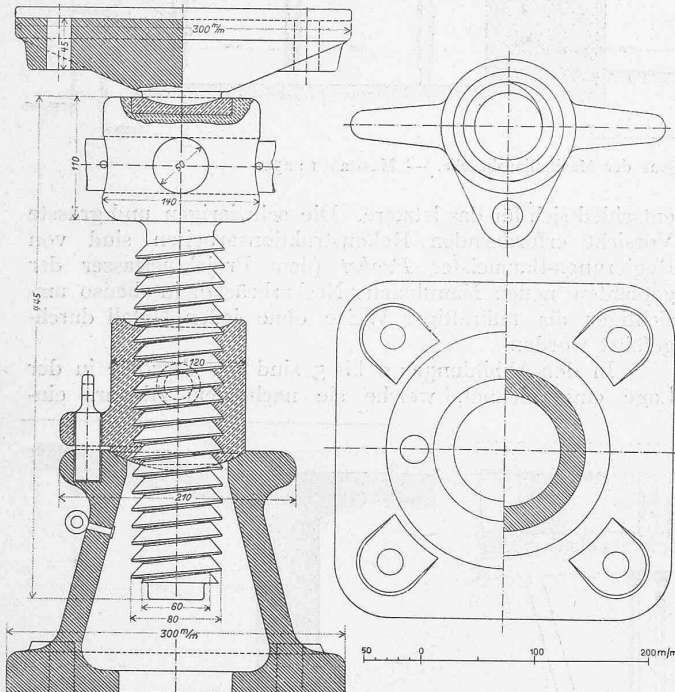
Senkschraube für das Lehrgerüst. — Masstab 1 : 6.
